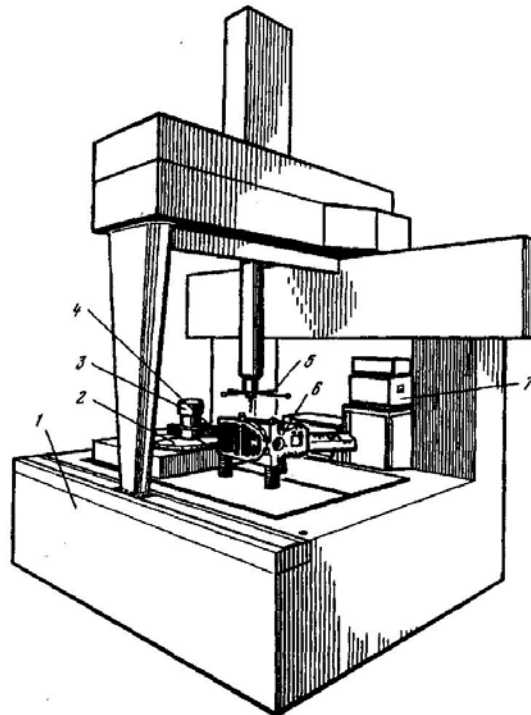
Координатно-вимірювальна машина: 1 – корпус, 2 – поворотний стіл, 3 – притискний пристрій, 4 – деталь, яка очікує вимір, 5 – інструментальні щупи, 6 – вимірювана деталь, 7 – система керування
